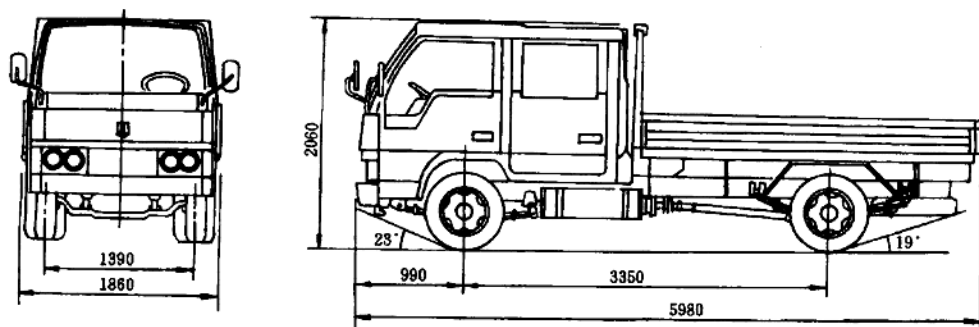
6 解放 CA1049L₂ 型载货汽车外形尺寸
